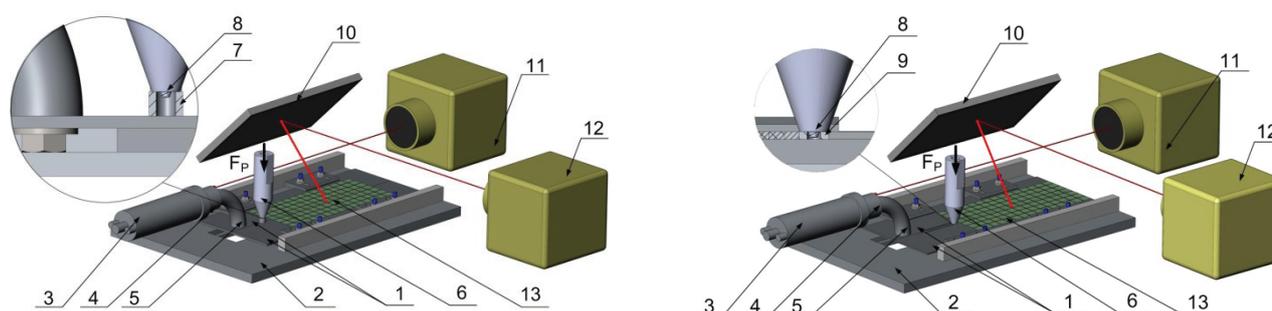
Схемы сканирования поверхности образца, моделирующие состояние перед началом сварки (а) и в процессе сварки (б):
